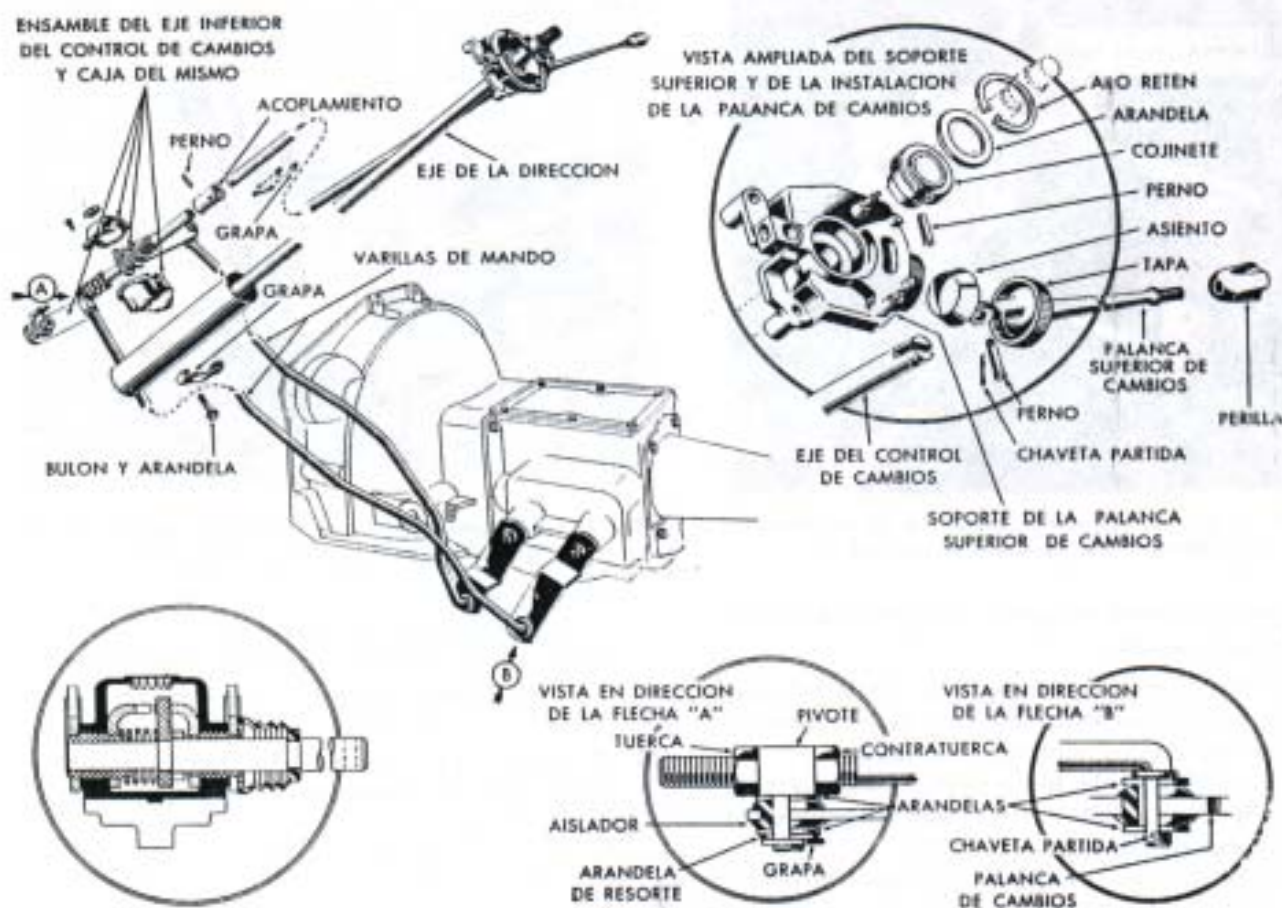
Despiece del Conjunto de la Caja Selectora de Cambios para "Carabela".
